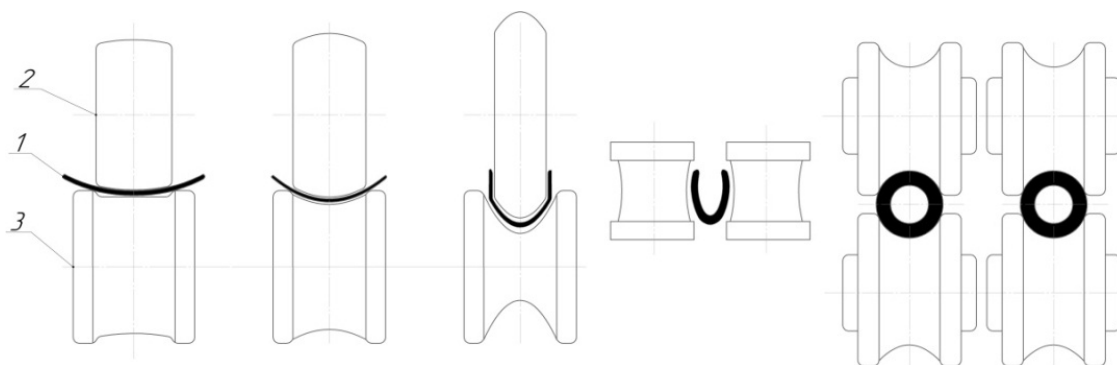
Звертання заготовки в трубу в неперервних станах дуо:
